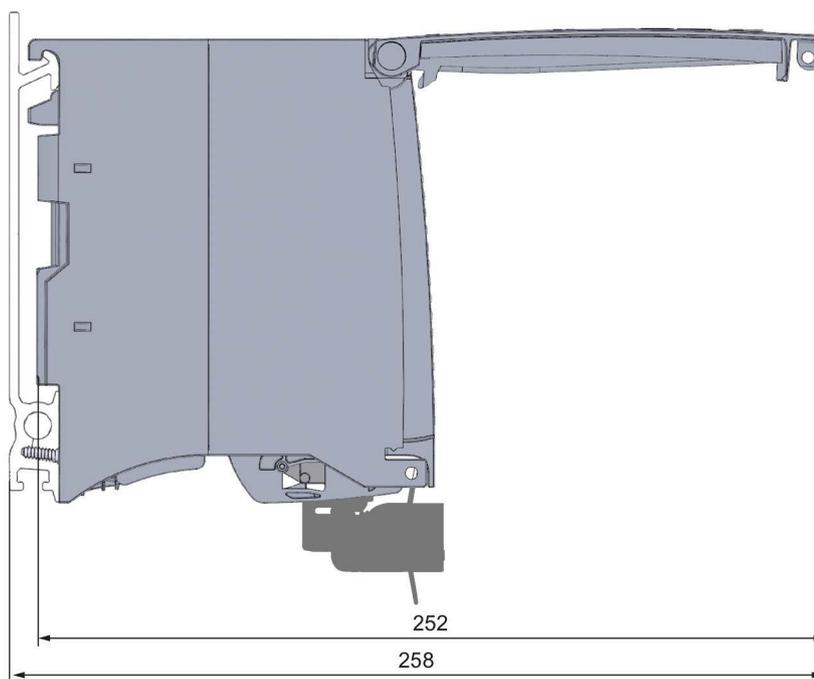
Dessin coté de la CPU 1511C-1 PN, vue de côté avec volet frontal ouvert
